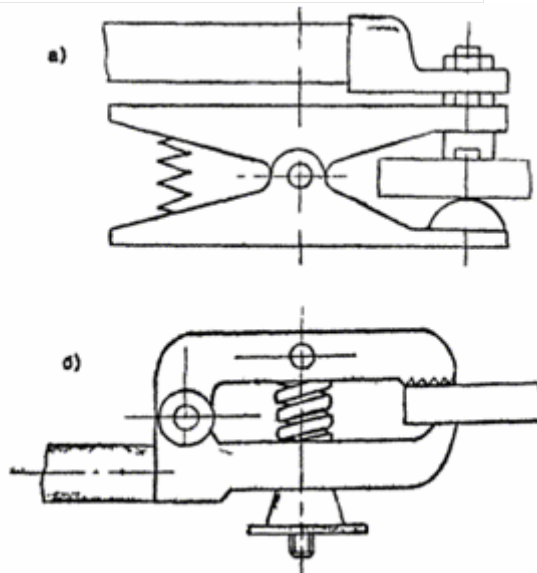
Зажимы для присоединения сварочного провода к свариваемому изделию:
